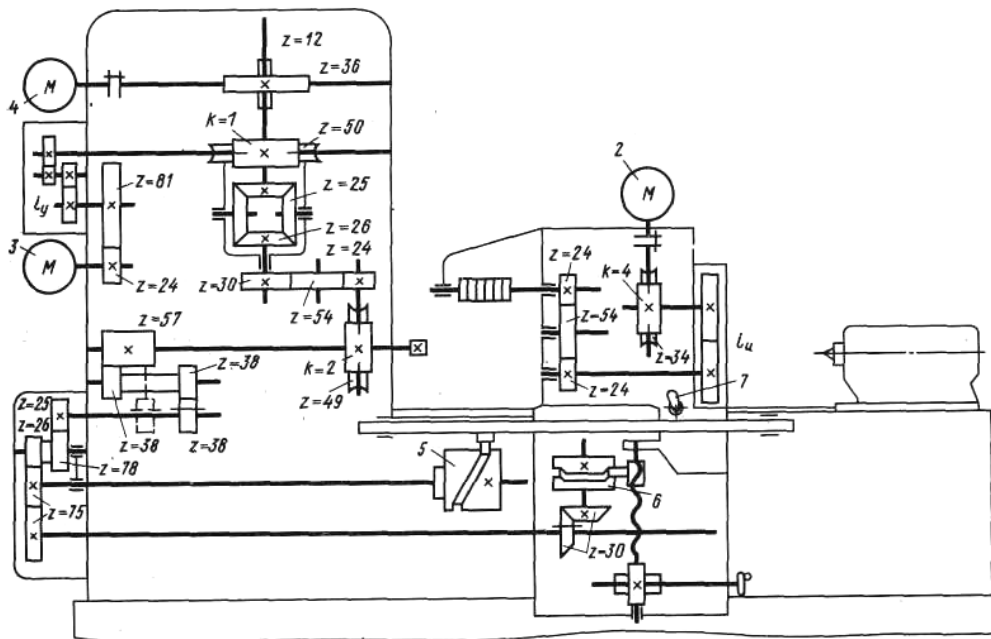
Кинематическая схема резьбофрезерного станка для обработки коротких резьб модели 5M5B62
